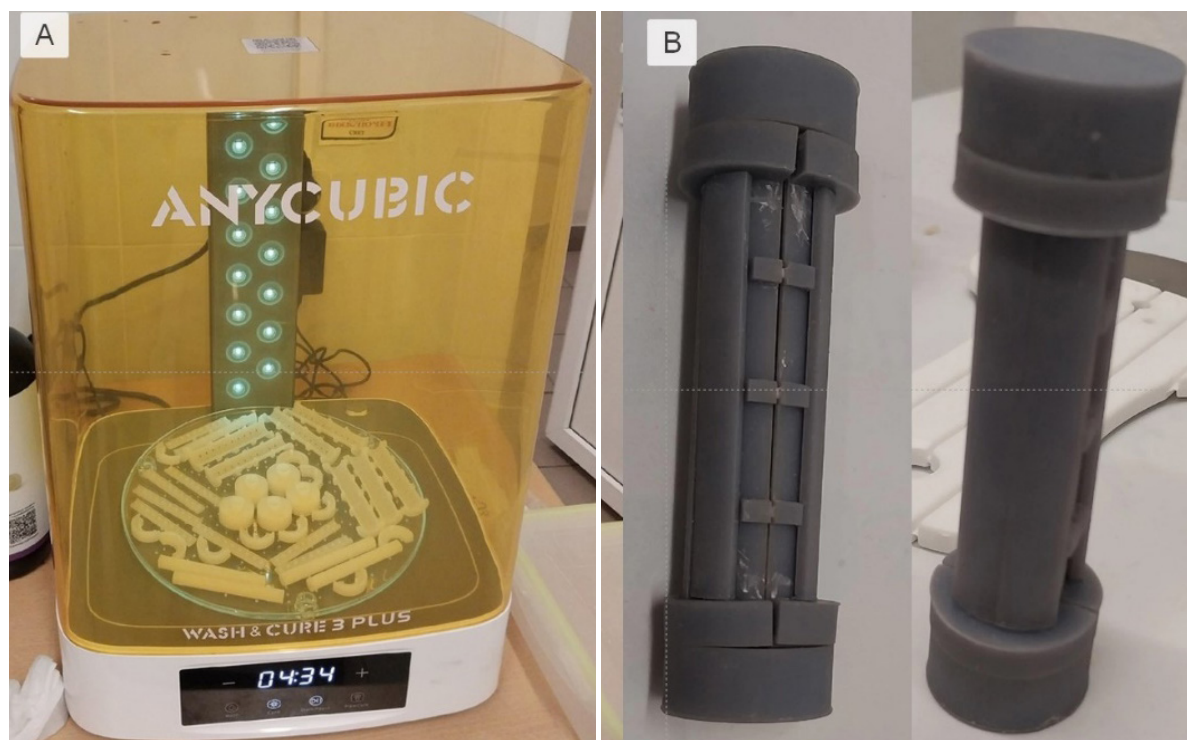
Процесс изготовления литейной формы. А — Постобработка деталей различных типов для 4-хлитейных форм, изготовленных из фотополимерной смолы HarzLabs Industrial Nylon-like. В — внешний вид литейной формы, изготовленной из фотополимерной смолы HarzLabs Dental Model Light Grey, в собранном состоянии
